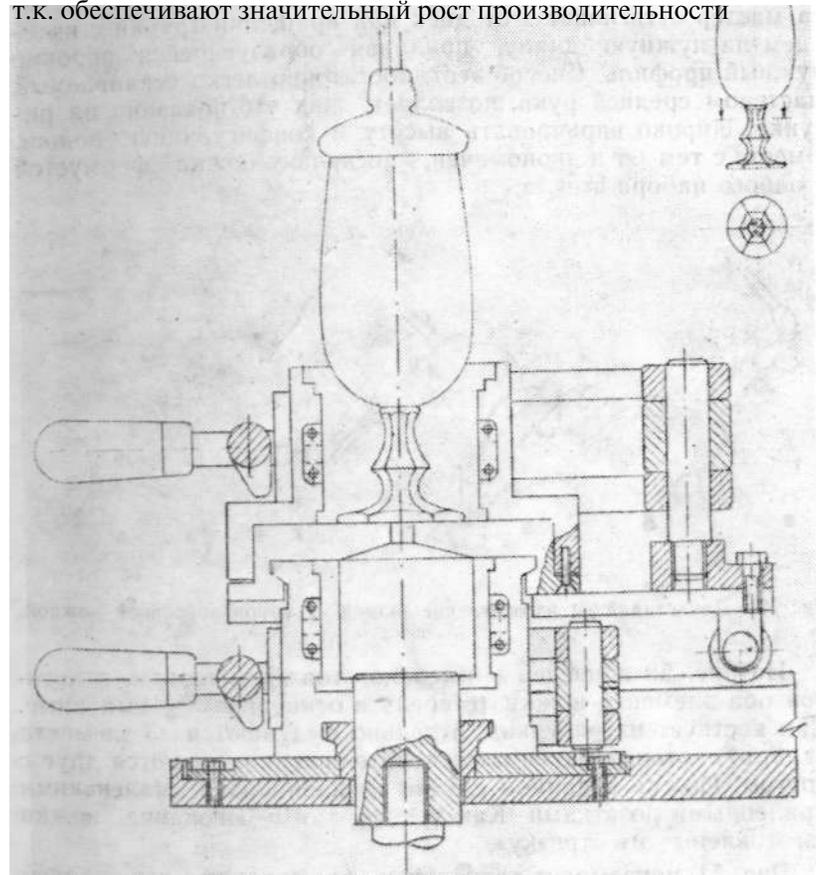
Рабочий узел пневматического пресса для подпрессовки всей ножки (стебля и основания).
